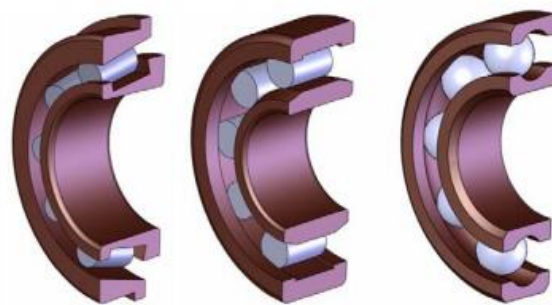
Несамоустанавливающиеся подшипники качения
